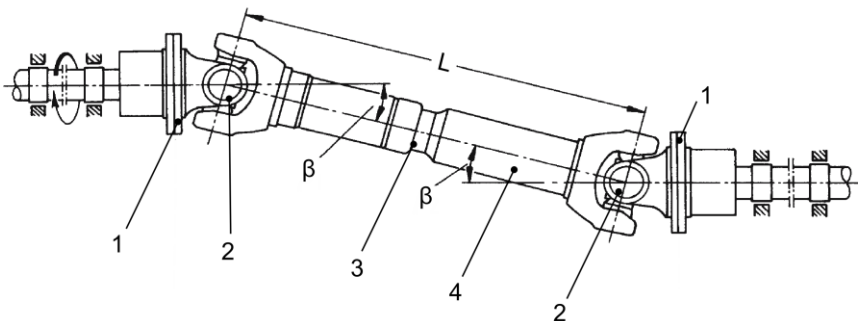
Aufbau einer Kreuzgelenkwelle: Der Aufbau besteht aus zwei Anschlussflanschen /1/, zwei Gelenken /2/, einem Längenausgleich /3/ und einem Verbindungsrohr /4/, welches in der Regel eingeschweißt wird. Abb. mit Änderungen entnommen aus Seherr-Thoss (15).
